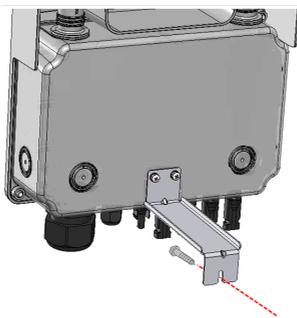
Fissare l'Unità di sicurezza CC alla parete
